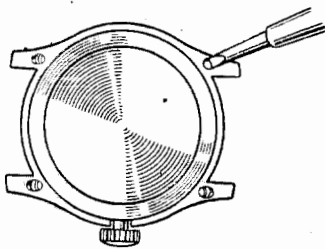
Американское универсальное приспособление «De Vries» для открывания корпусов.
